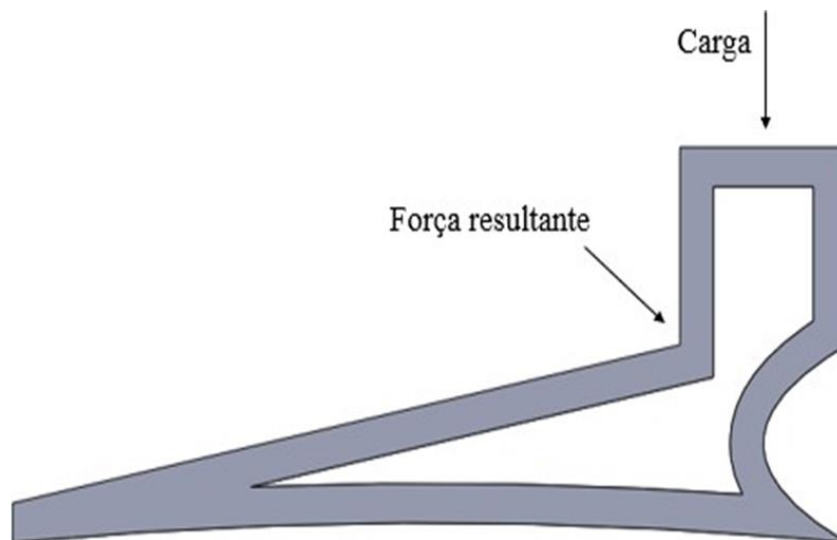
Desenho do perfil e das dimensões da primeira geometria.
